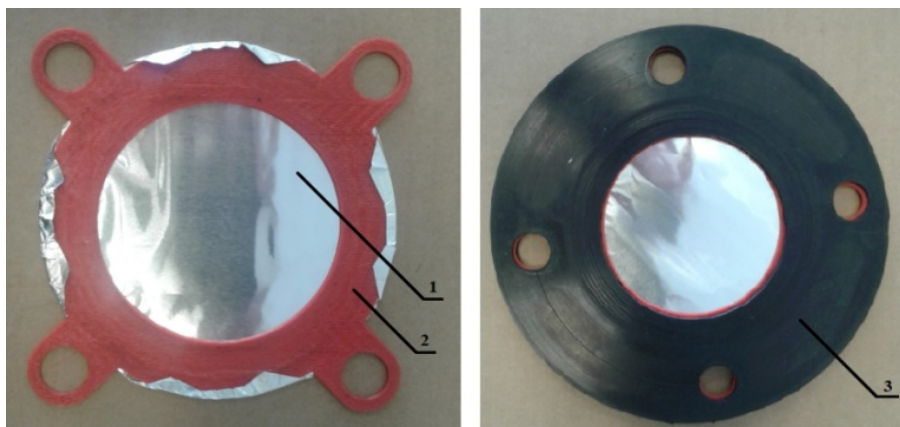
Prototipo TC-02-(0.4/2): montaje del diafragma.
